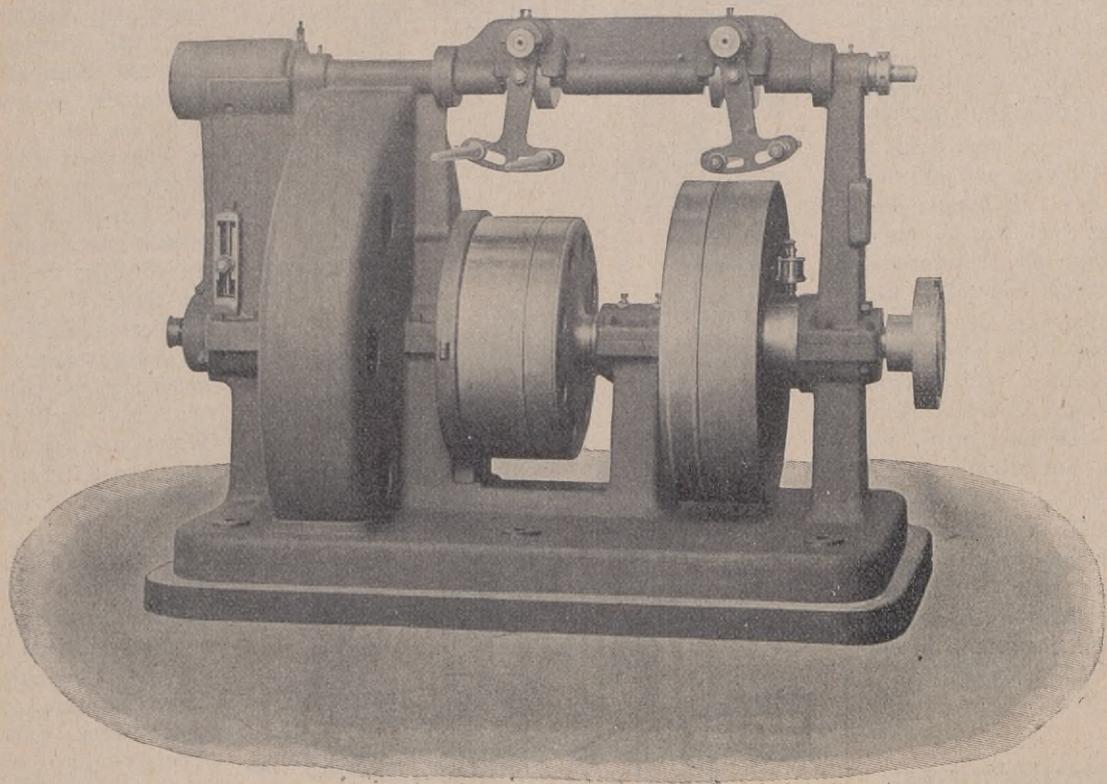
(Zu Hülfssteuerung für Werkzeugmaschinen.)
